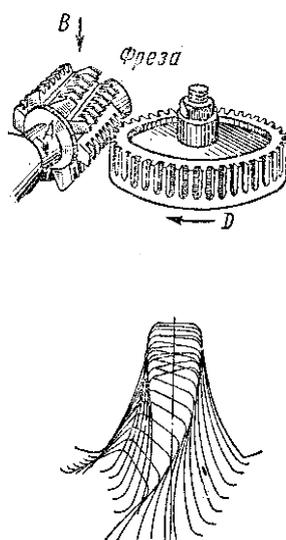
Схема зубофрезерования зубчатых колес методом обкатки
